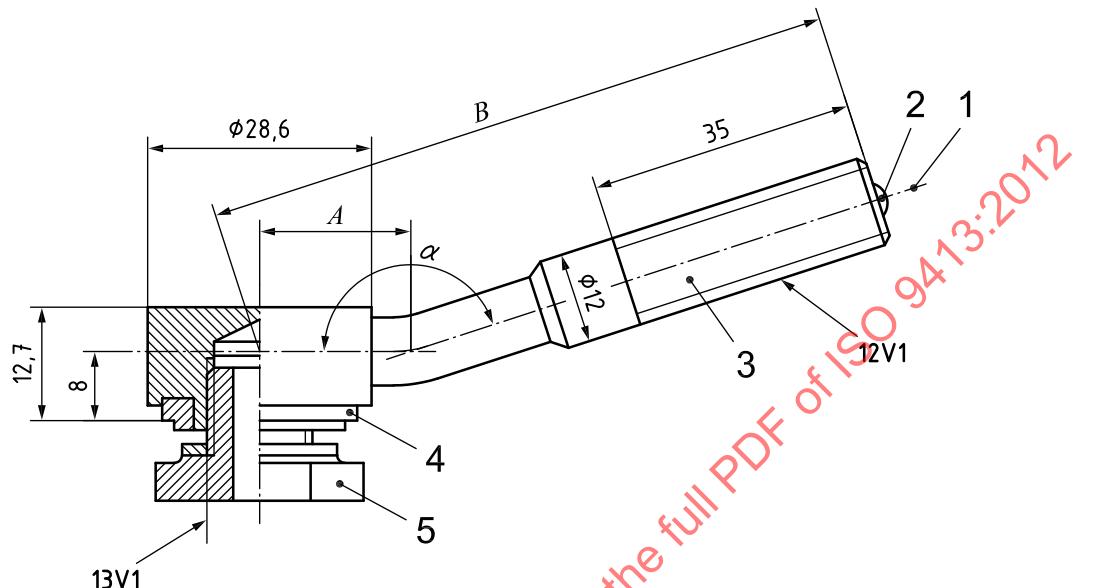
Montage de la valve tubeless air/liquide pour trou de valve pour la jante  $15,7^{+0,4}_0$
